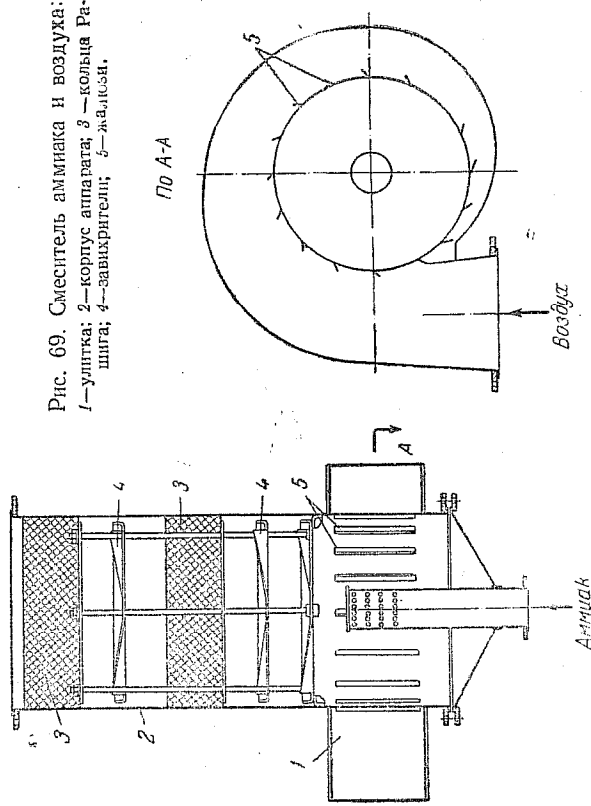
Смеситель аммиака и воздуха: 1—улитка; 2—корпус аппарата; 3—кольца Раундиша; 4—завихрители; 5—жало.
